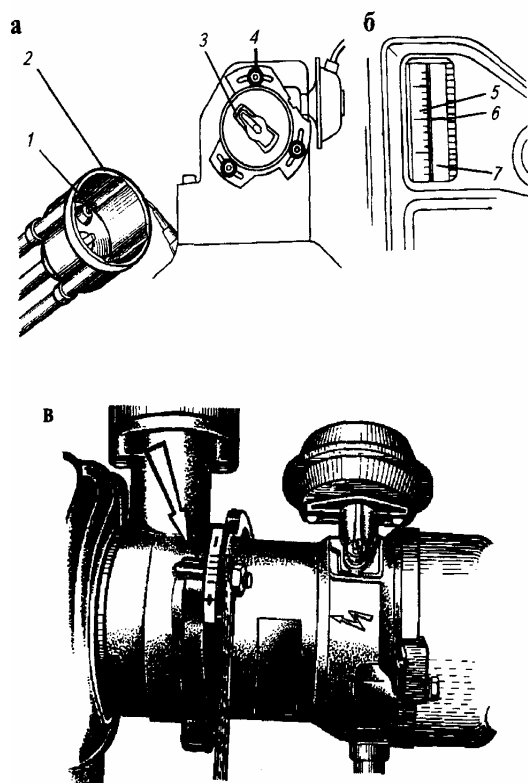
Проверка момента зажигания (искрообразования) на автомобиле ВАЗ-2108, 2109: а - датчик-распределитель; б - люк в картере сцепления; в - установка датчика-распределителя (стрелкой показан установочный выступ на корпусе вспомогательного агрегата); 1 - боковые контакты крышки распределителя; 2 - крышка распределителя; 3 - ротор; 4 - гайка крепления корпуса датчика; 5 - шкала; 6 - метка на маховике; 7 - люк
